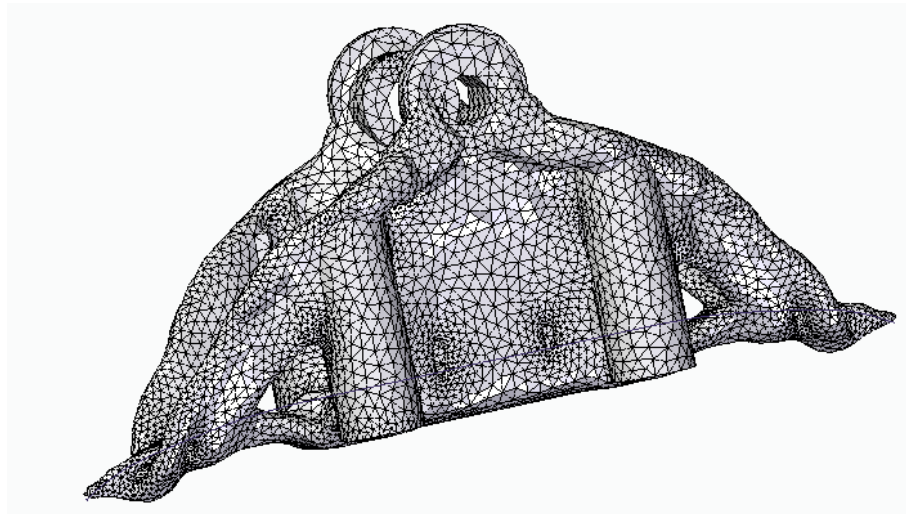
Mallado al 48%. Fuente: elaboración propia
